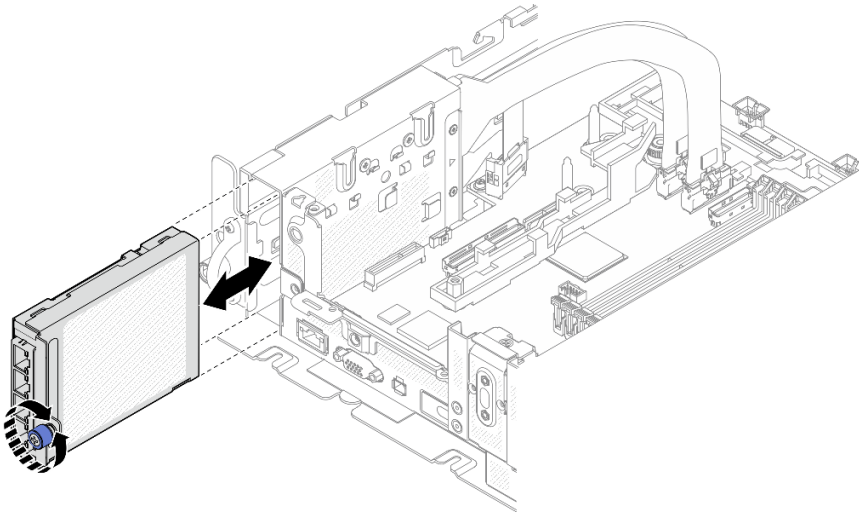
Entfernen des OCP-Ethernet-Adapters
